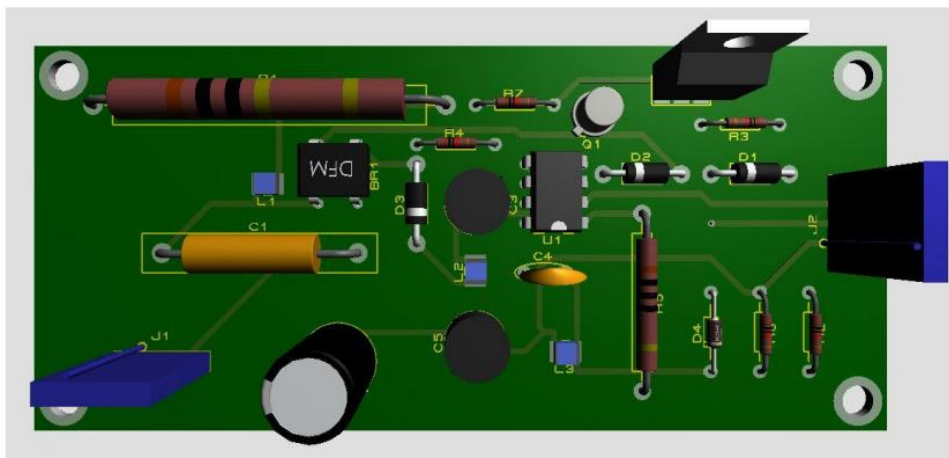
Зовнішній вид друкованої плати з встановленими компонентами пристрою
